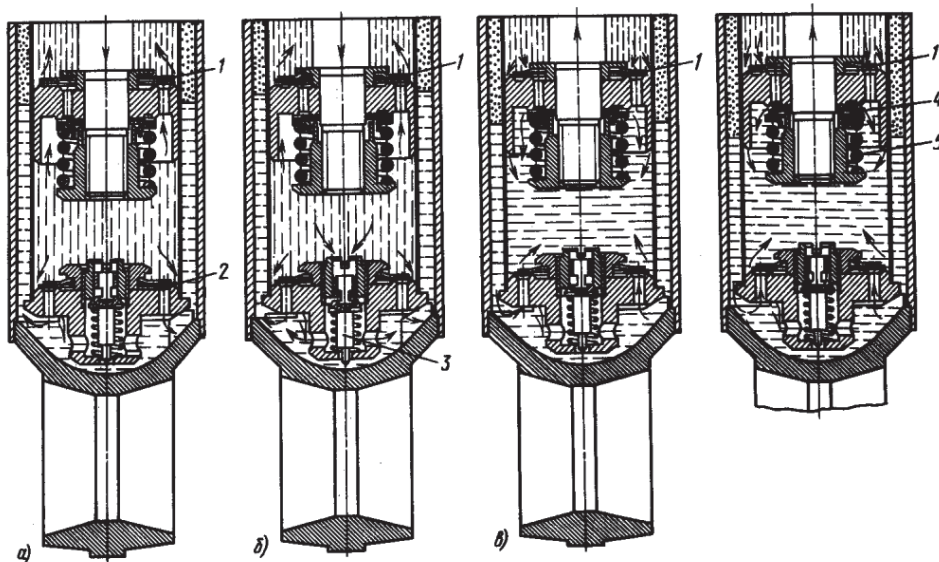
Робочий процес двотрубного телескопічного амортизатора:
